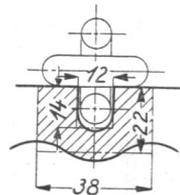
Zur Berechnung der Beanspruchung der Trommelwandung.
